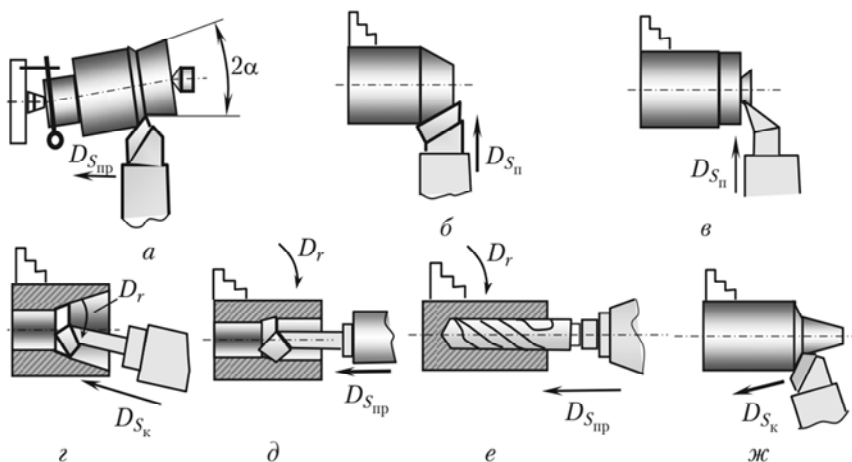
Некоторые схемы обработки поверхностей заготовок на токарно-винторезном станке:
